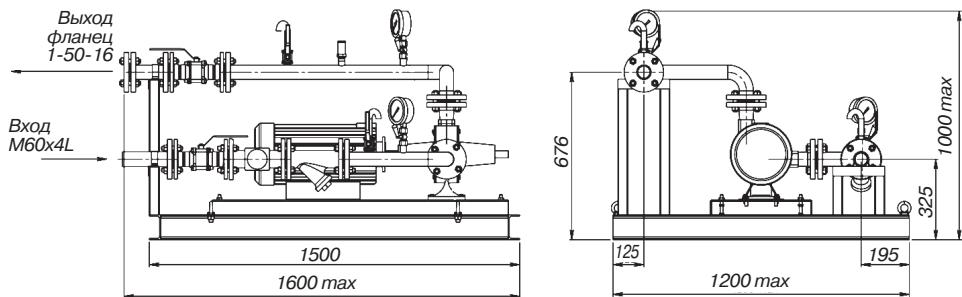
Габаритно-присоединительный чертеж установки насосной Vortex
